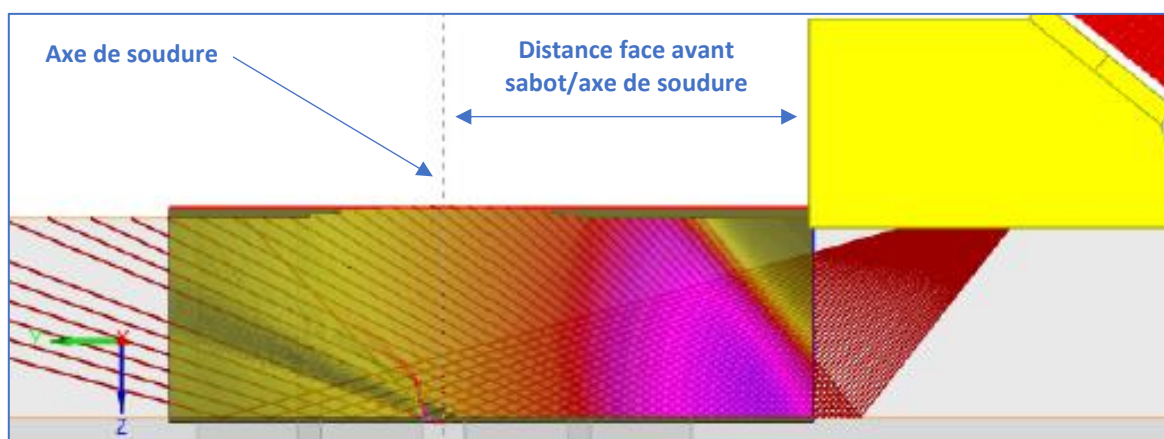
Distance face avant sabot/axe de soudure
